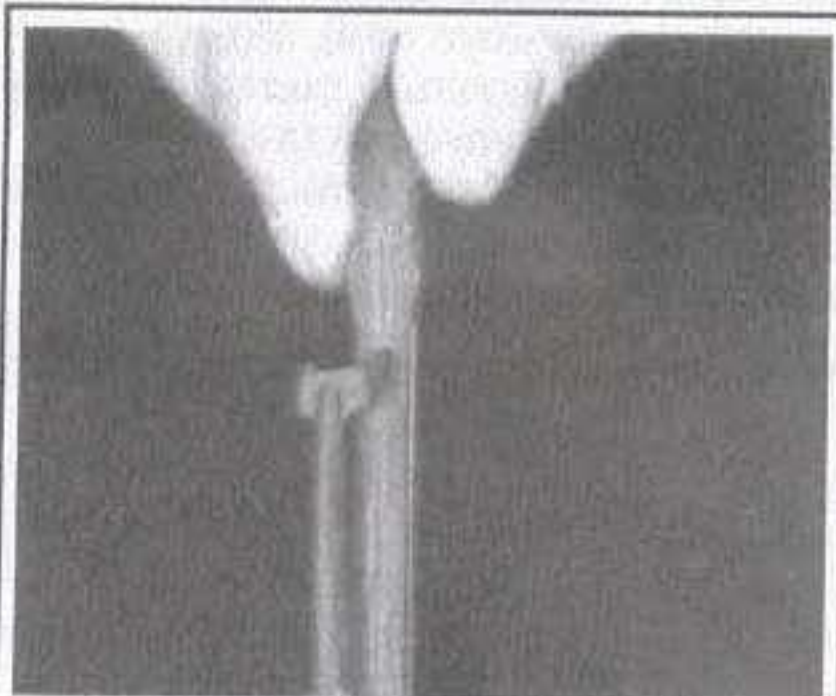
затем выведите фиксатор из прямоугольного отверстия и выньте резиновую щетку вместе с двумя металлическими опорами из щеткодержателя в сборе
